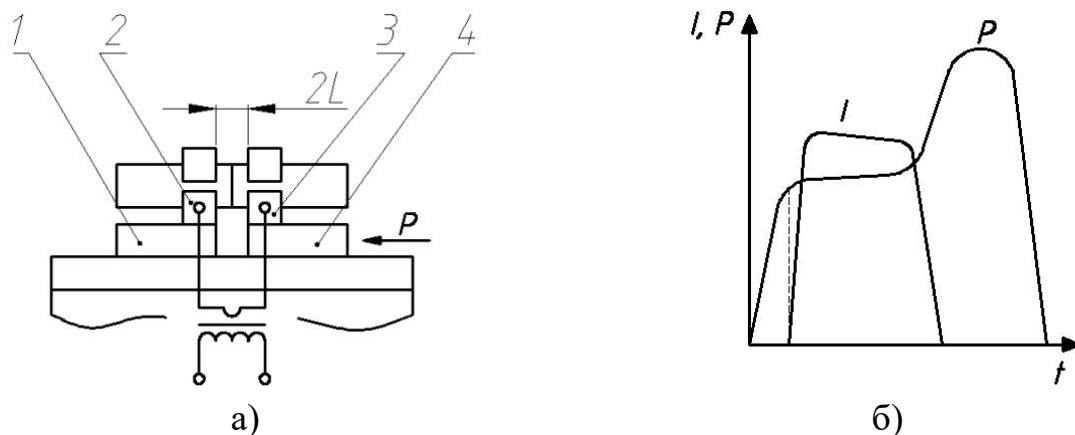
Схема контактної стикової зварювання (а) та циклограма контактної зварювання опором (б)
